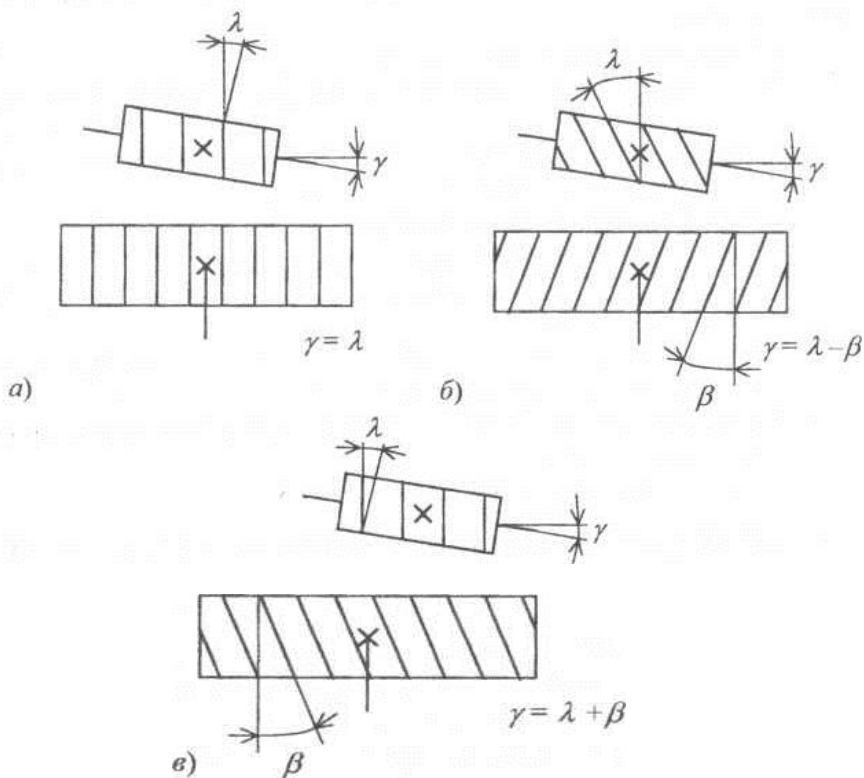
Схема взаємного розташування фрези на оправці та салазок фрезерного супорта
